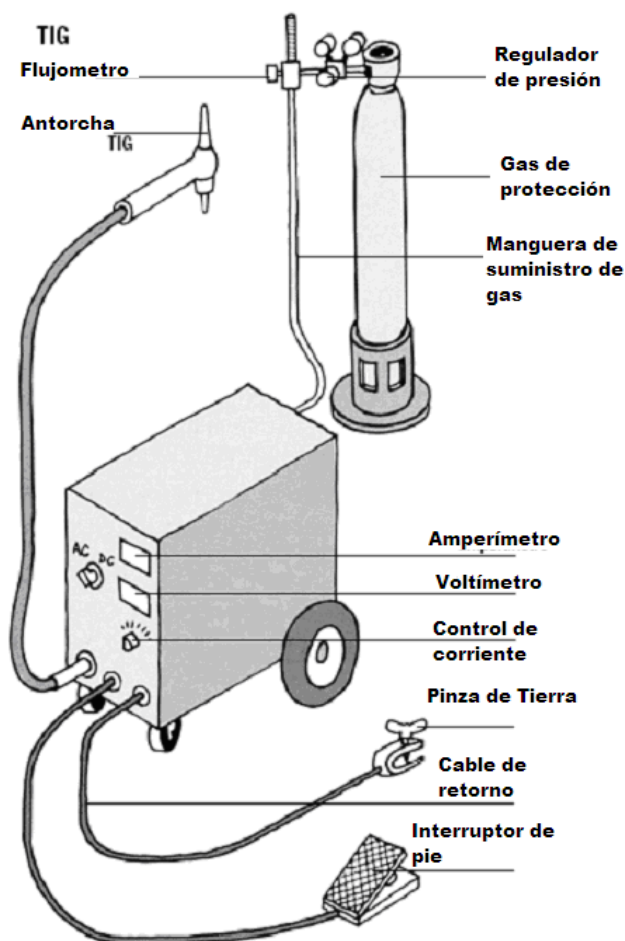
Circuito de soldadura para el proceso GTAW
